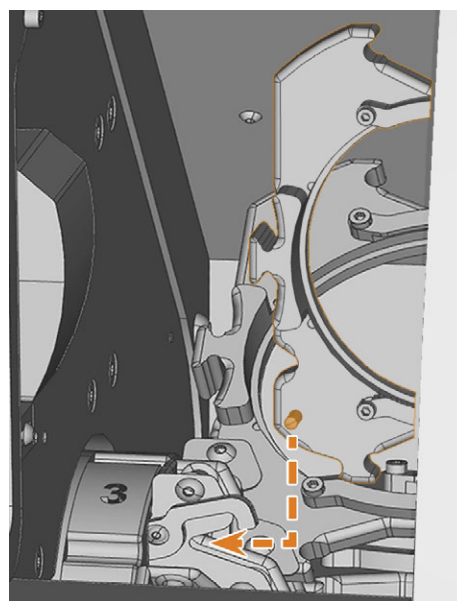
INSERTION DU CADRE DE PIÈCES BRUTES DANS LE MAGASIN DE PIÈCES BRUTES
